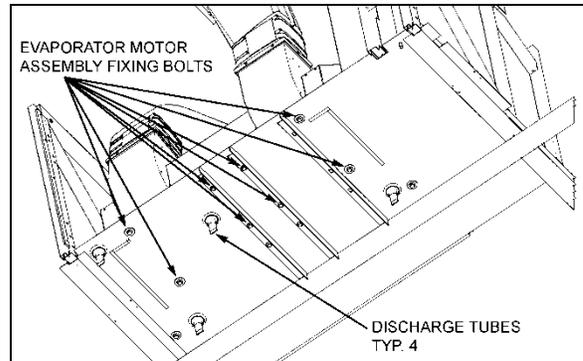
PERNOS DEL MOTOR DEL EVAPORADOR
